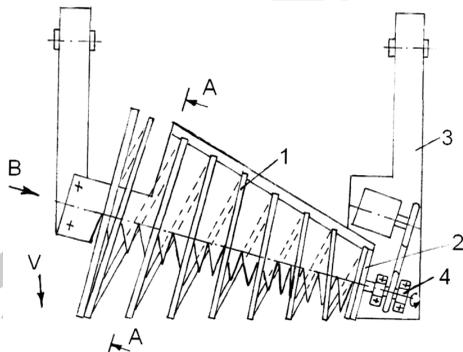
Режущий аппарат косилки травы (вид сверху)
